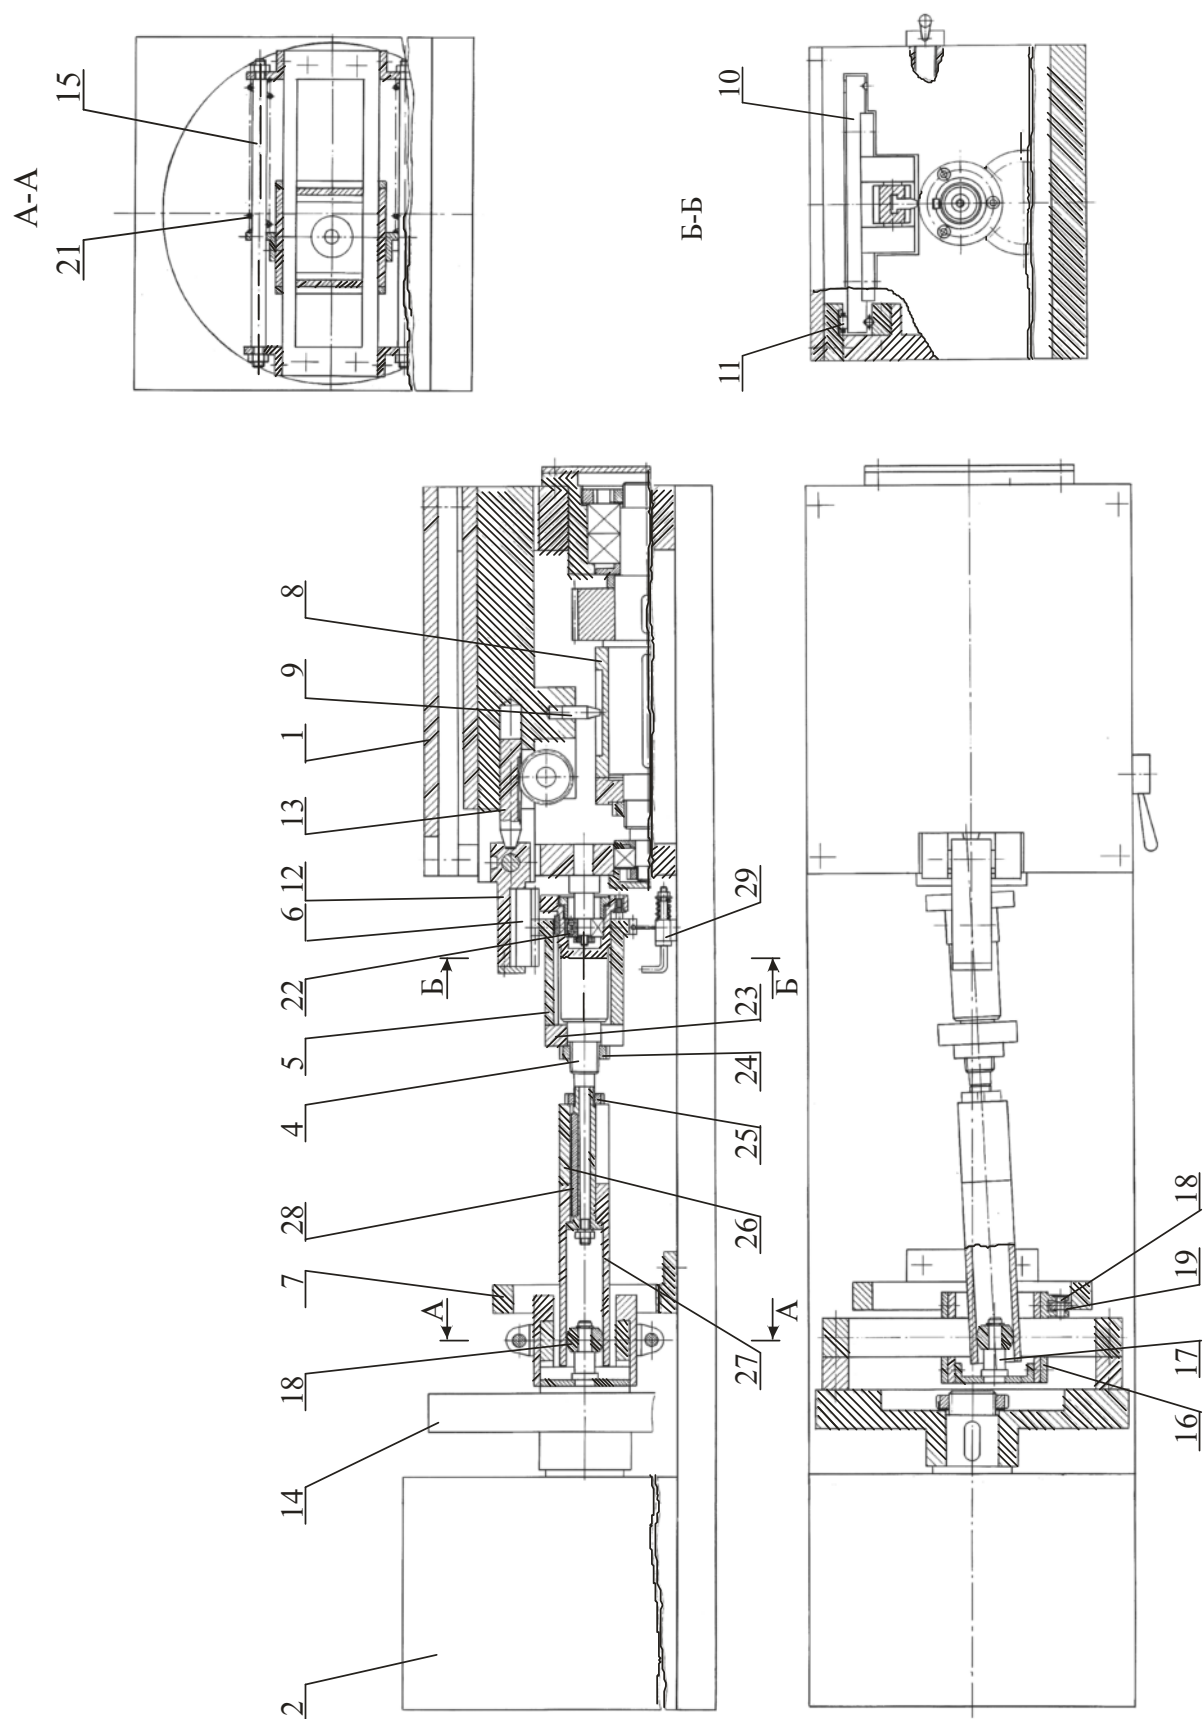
Общий вид устройства для чистовой обработки зубьев с пространственной геометрией
